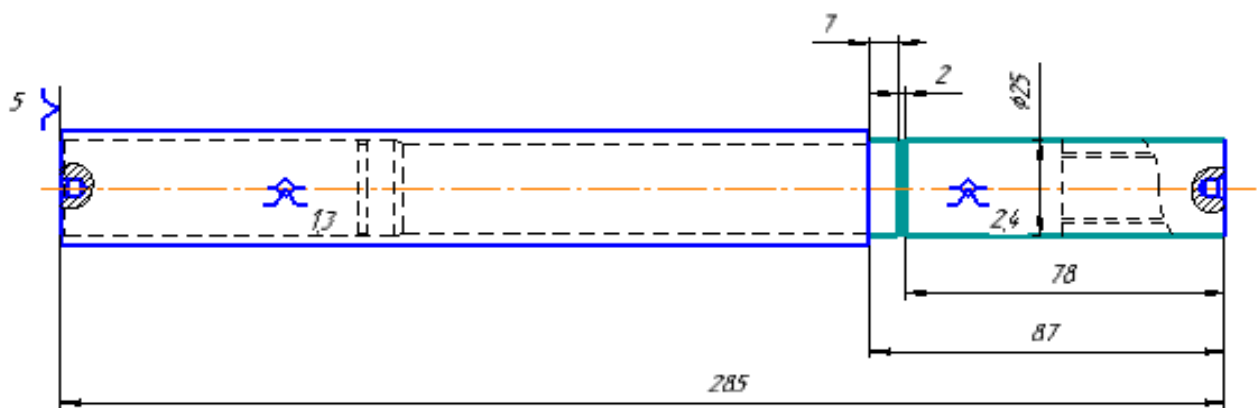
Обробка деталі при токарно-багаторіздевій операції.
